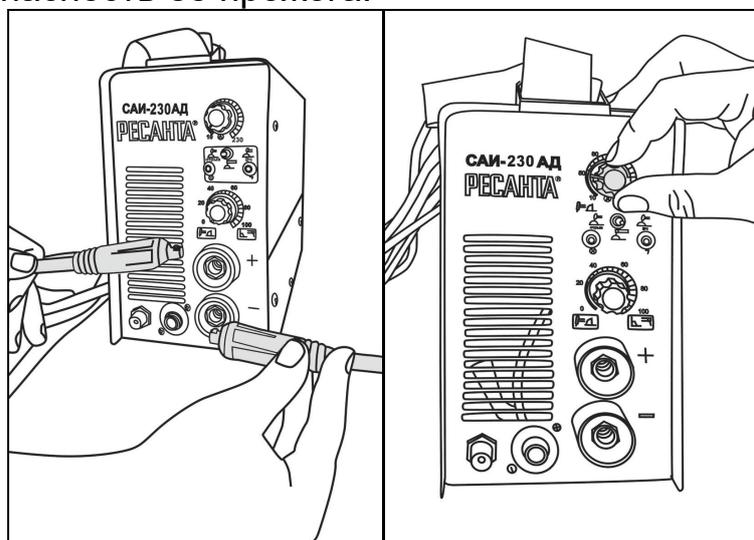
Подключение кабелей и выставление режимов сварки
